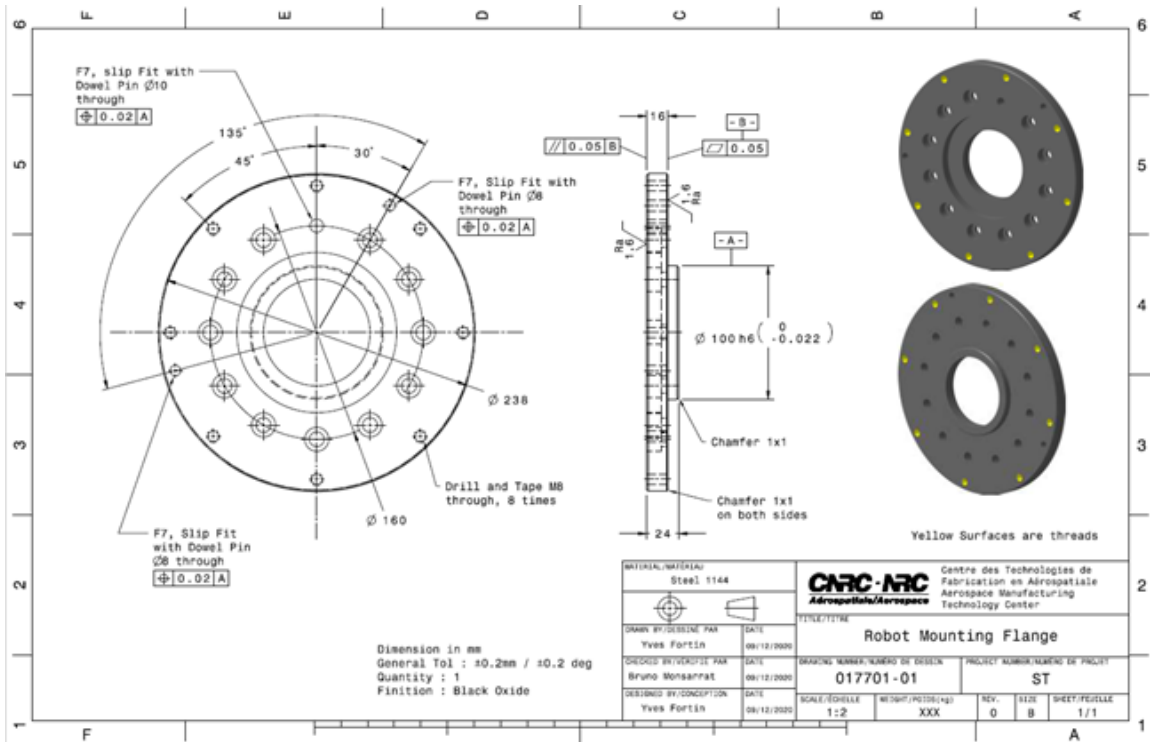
Dessin technique de la bride 2, fourni par le CNRC
